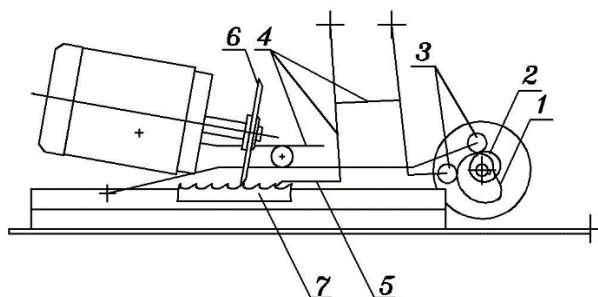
Схема двух кулачковой заточной устройства станка с ЧПУ 3к-327«Тайга»
